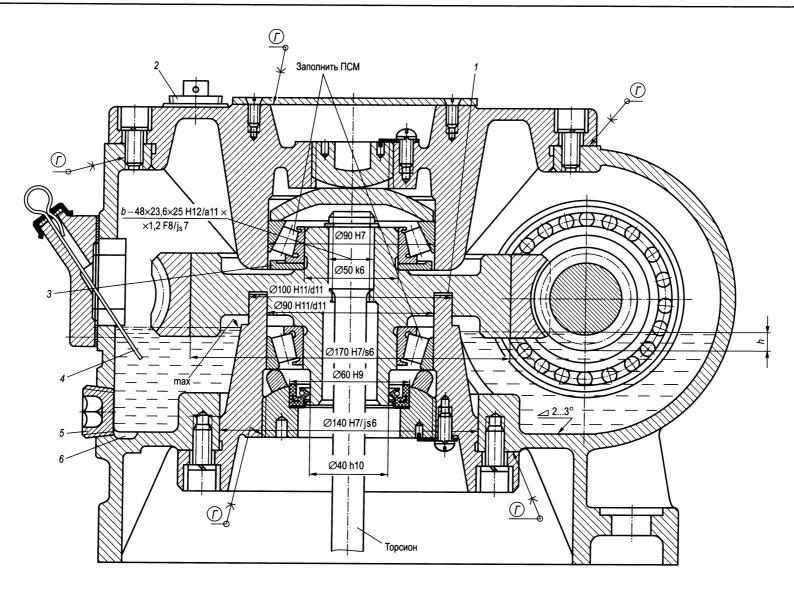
Червячный редуктор с вертикальной осью червячного колеса и погружением червяка в масляную ванну на глубину h = 3m:
